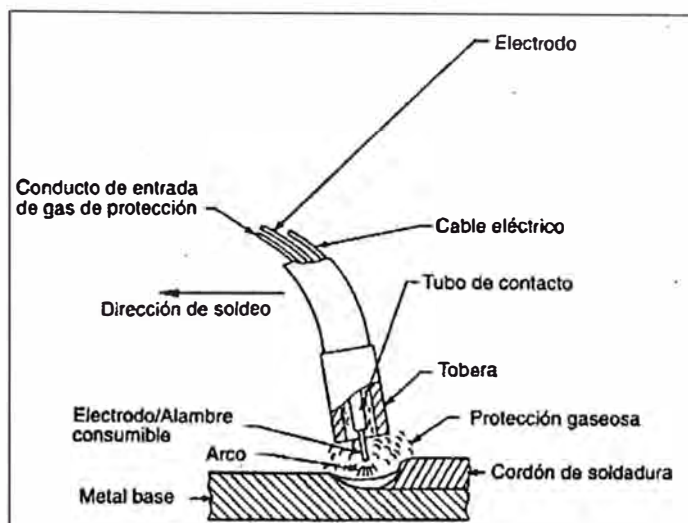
Esquema de soldadura GMAW
